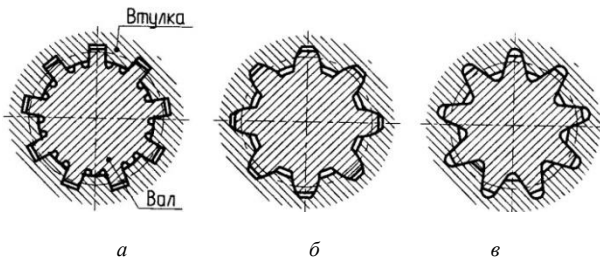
Профиль шлицев: *а* – прямоугольный; *б* – эвольвентный; *в* – треугольный
